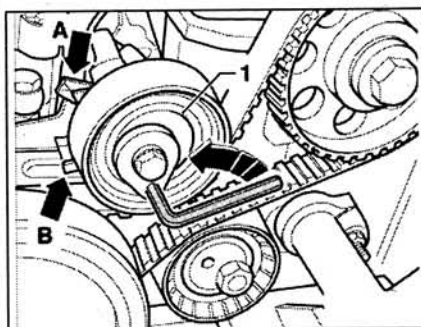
а. Установите натяжной ролик 1 так, чтобы ушко на нем установилось в паз на консоли (стрелка В). Натяните зубчатый ремень, прокрутив натяжной ролик против часовой стрелки так, чтобы две метки расположились друг напротив друга (стрелка А).
